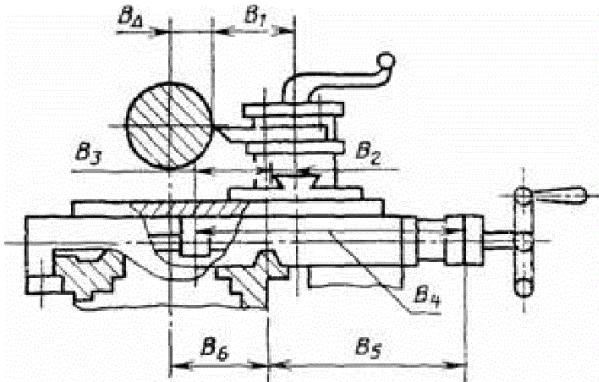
Размерная цепь В, определяющая размер B_{Δ} радиуса валика, изготовляемого на токарном станке
